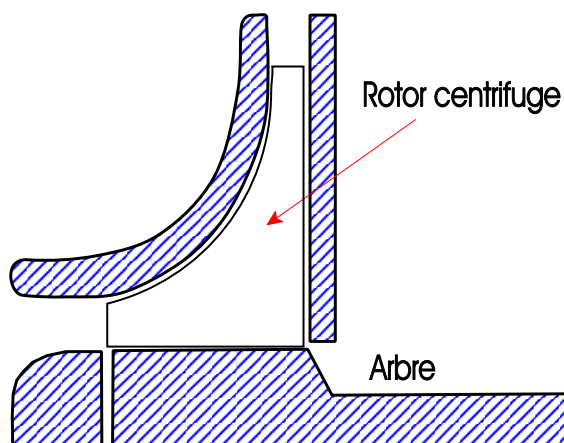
Coupe axiale($r - z$) d'une machine radiale
